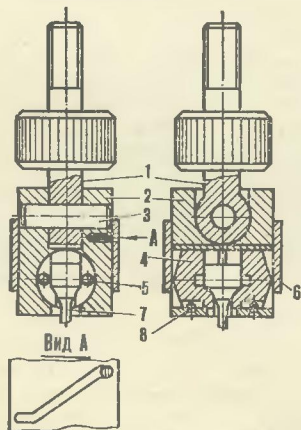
Схема зажима: 1 — тяга испытательной машины, 2 — корпус зажима, 3 — соединительная ось, 4 — вкладыш, 5 — пружина, 6 — стяжное кольцо, 7 — испытуемый образец, 8 — стопорный винт.
